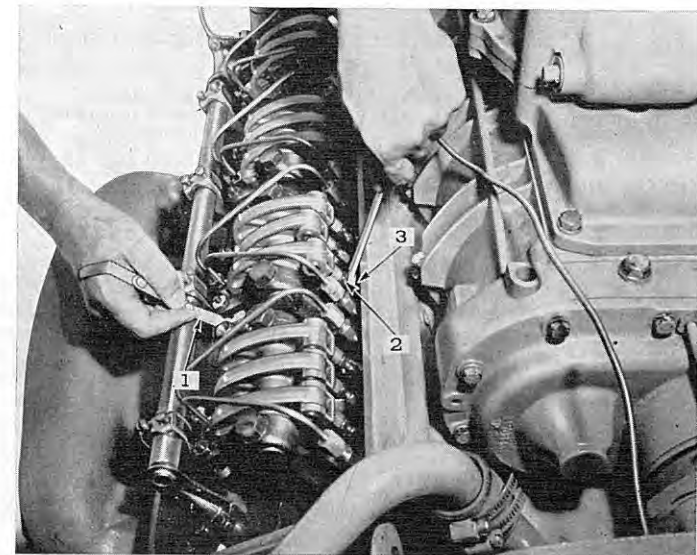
Réglage du jeu de soupapes (4 soupapes) avec
